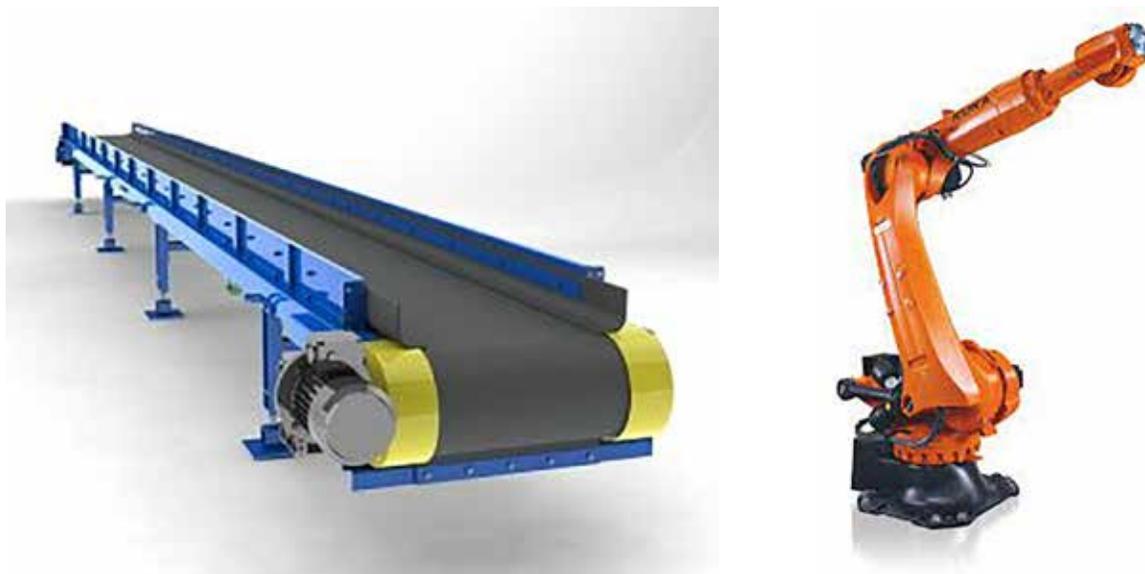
Пример конвейера и робота, используемых для сборки редуктора
